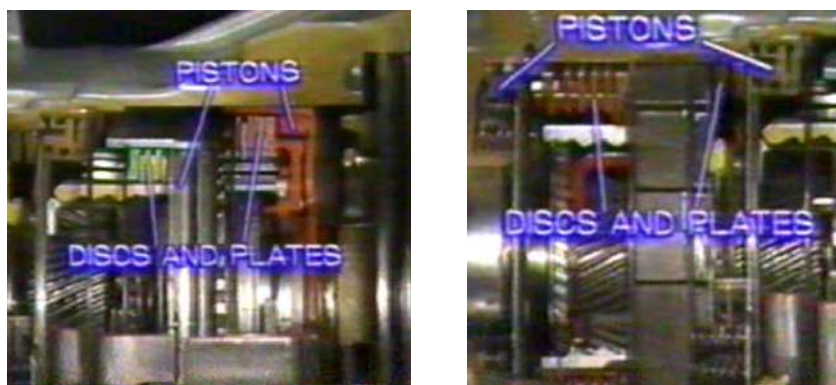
Bodi Transmisi Dan Gear Unit.
